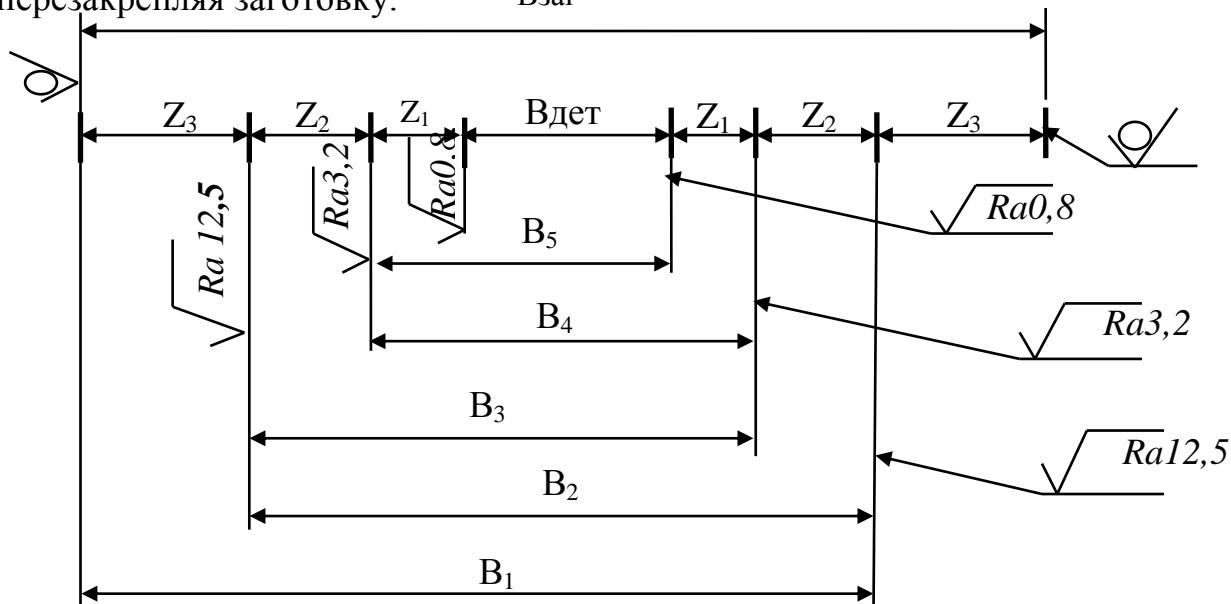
Расчетная схема для вычисления межоперационных размеров при обработке торцевых поверхностей, при разделении черновых и чистовых операций. Вдет – размер готовой детали; Взаг – размер заготовки;  $Z_1$  – припуск на окончательную обработку;  $Z_2$  – припуск на чистовую обработку;  $Z_3$  – припуск на черновую обработку;  $B_1, B_2$  – размеры после черновой обработки;  $B_3, B_4$  – размеры после чистовой обработки;  $B_5$  – размер после окончательной обработки одного торца.
